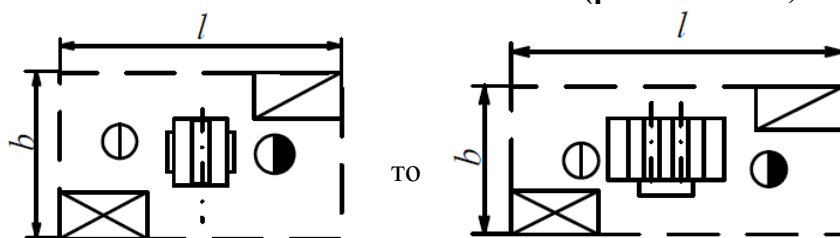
Рабочее место станка CP3-6(7) станка C2P8-3
